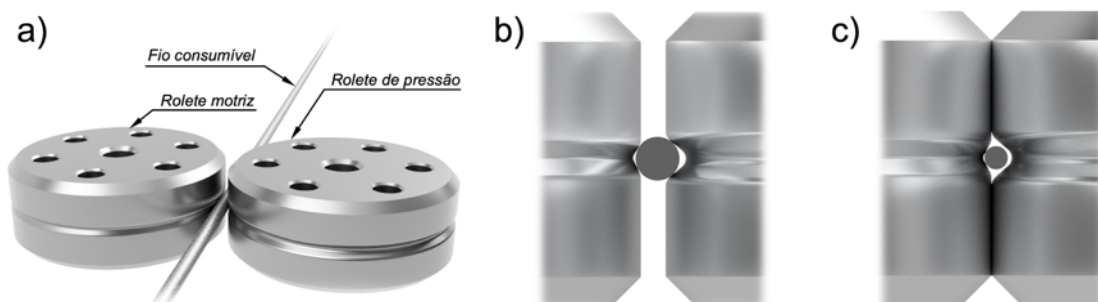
Ilustração do escorregamento de fio de soldadura no mecanismo de tração da máquina de soldadura:
